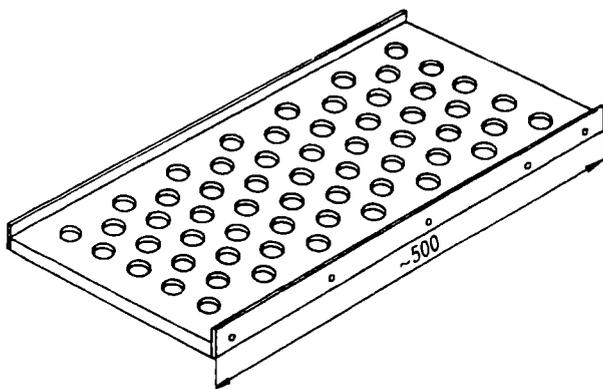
Приспособление для выделения крошки из короткорезанных вермишели и лапши
